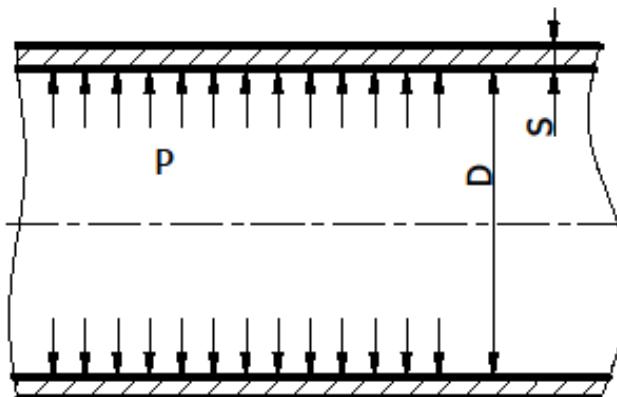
Розрахункова схема циліндричної обичайки
